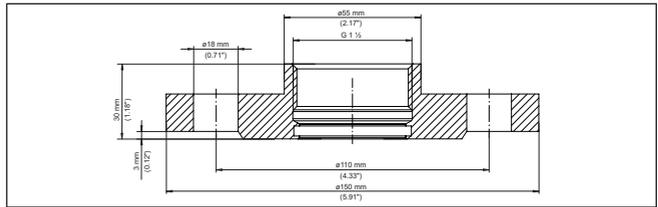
Medidas adaptador de rosca G1¼ (DIN 3852-X) em flange DN 40 (EN 1092-1, forma B1) PN 40
